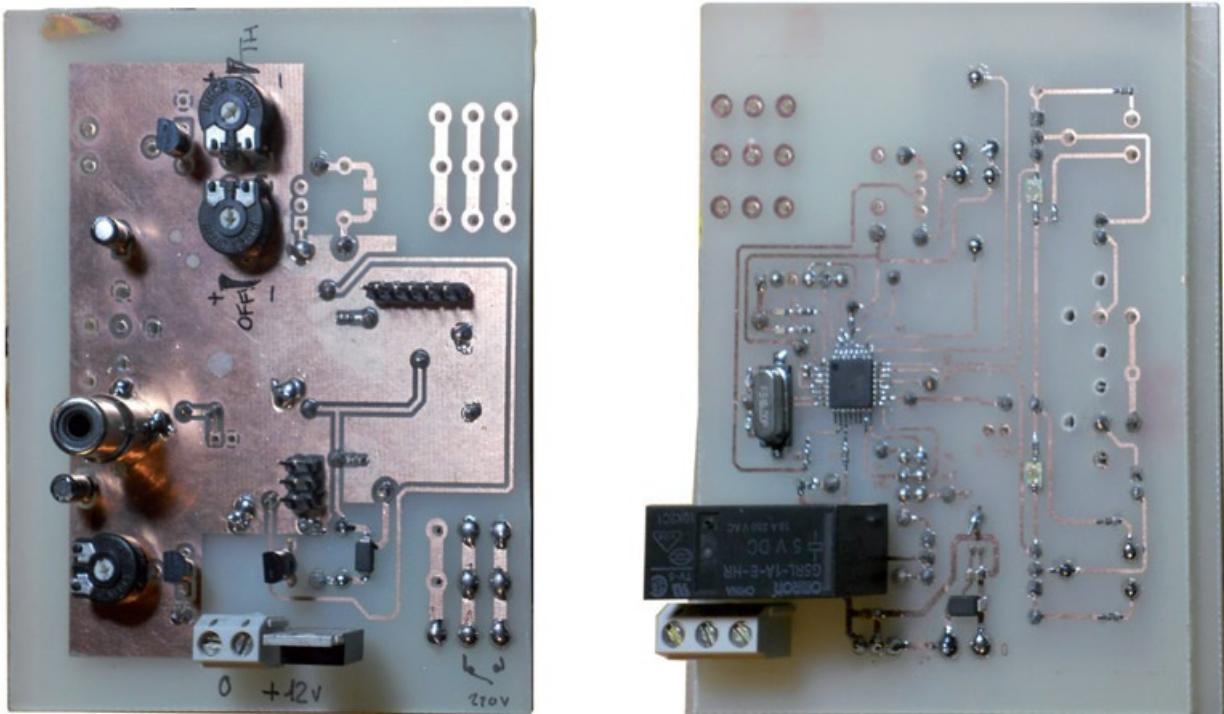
Circuito impreso de doble cara creado con la técnica del bocadillo.
